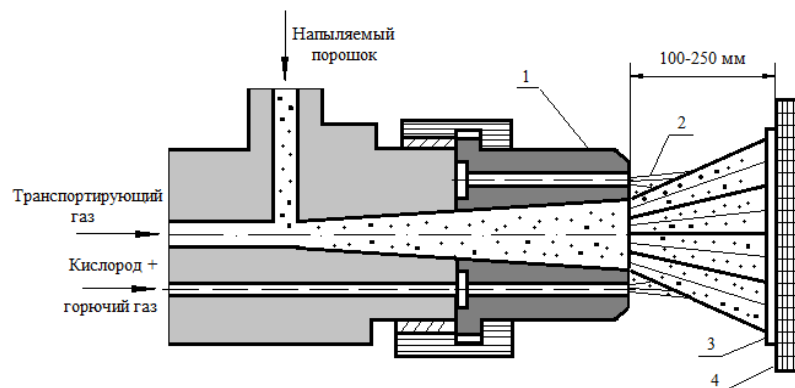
Газопламенное напыление порошкового материала: 1 - сопло; 2 - факел; 3 – покрытие; 4 – подложка
